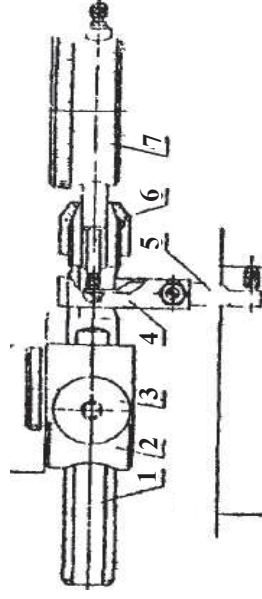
Установка блока для расточки по приспособлению с индикатором: 1 – стержень оправки; 2 – головка приспособления; 3 – винт крепления стержня; 4 – хомутик; 5 – мерительный рычаг; 6 – цанговый зажим; 7 – индикатор часового типа
